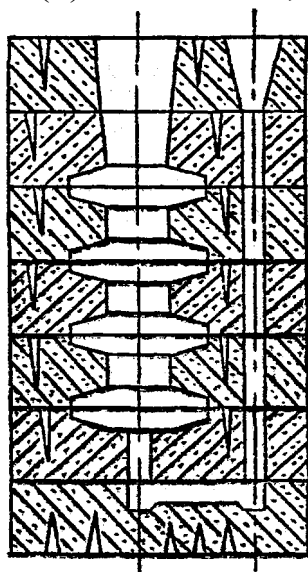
Схема стопочной формовки дисковых фрез
